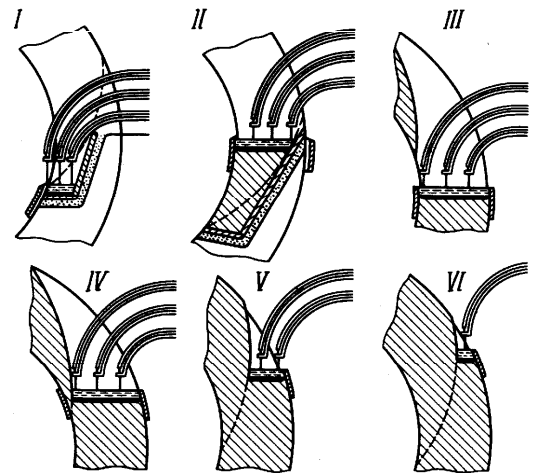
Последовательность этапов сварки кольцевого стыка
